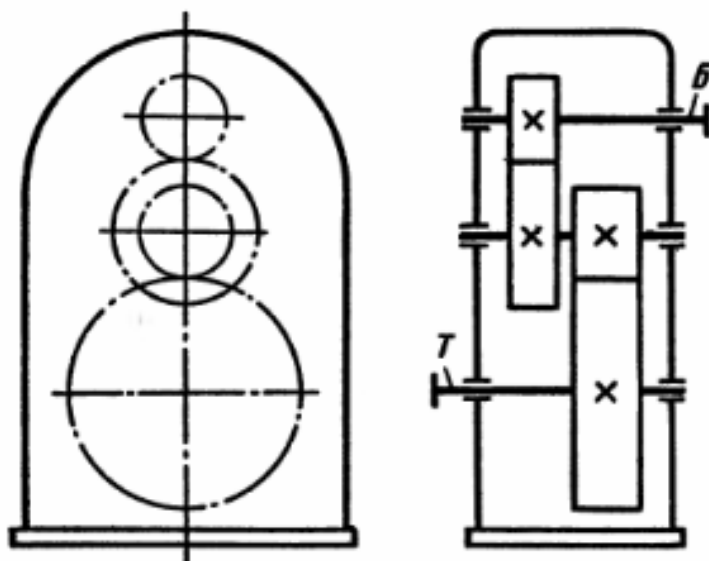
Схема цилиндрического двухступенчатого вертикального редуктора
